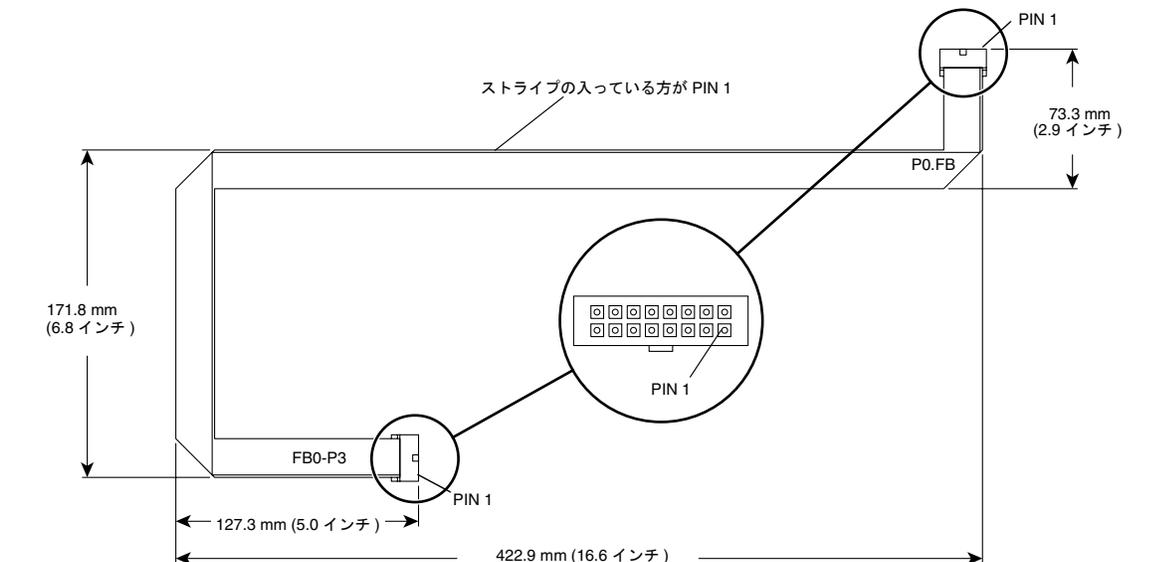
Fan I²C Cable、Front Lower (パーツ番号 530-2768)
